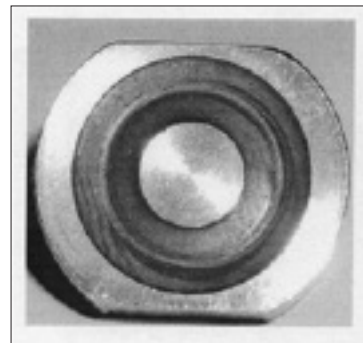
Канавка на резиновой поверхности уплотнительной вставки запорного узла клапана, которая образовалась после 90% выработки ресурса клапана
